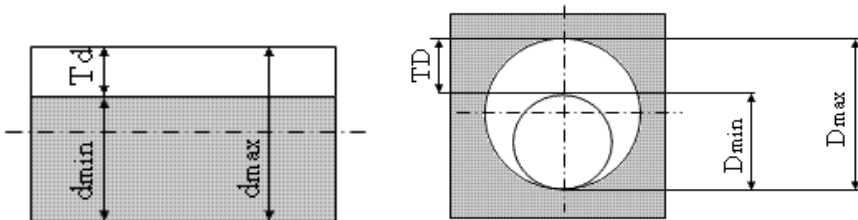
Допуск изготовления вала и отверстия.
